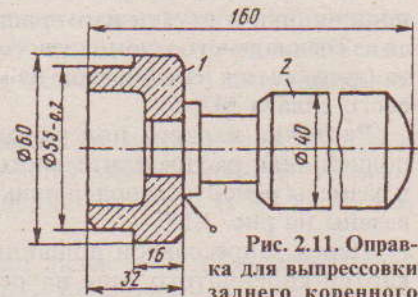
Оправка для выпрессовки заднего коренного подшипника: 1 - оправка; 2 - ручка оправки
